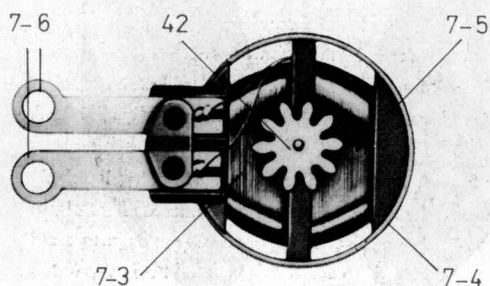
Motor U. (Schrittmotor) Ausf. II
